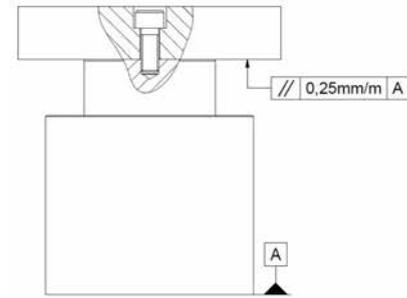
위치 지정을 위한 나사 연결 허용, 인장 하중 및 횡력 허용되지 않음. 나사산 깊이 감소만 가능합니다.
